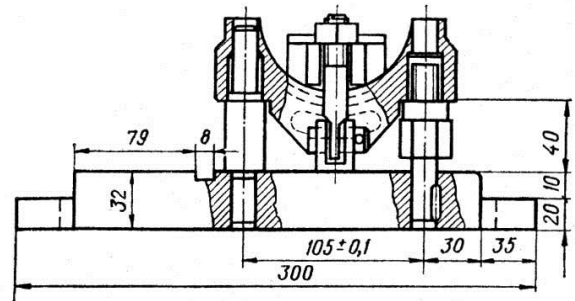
Пристрій для встановлення кришки шатуна під час фрезерування (шліфування) поверхонь рознімання.
